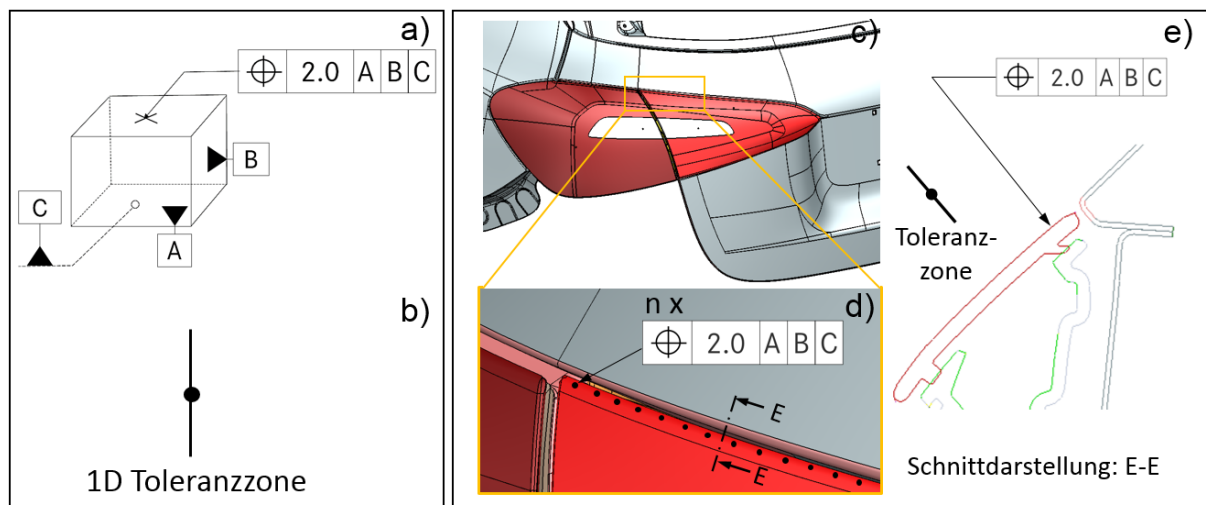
a) Theorie zum Punkt auf einer Fläche; b) Toleranzzone; c) Praxisbeispiel; d) Tolerierung der ausgewählten Punkte auf der Randfläche; e) Schnittdarstellung der Heckleuchte
